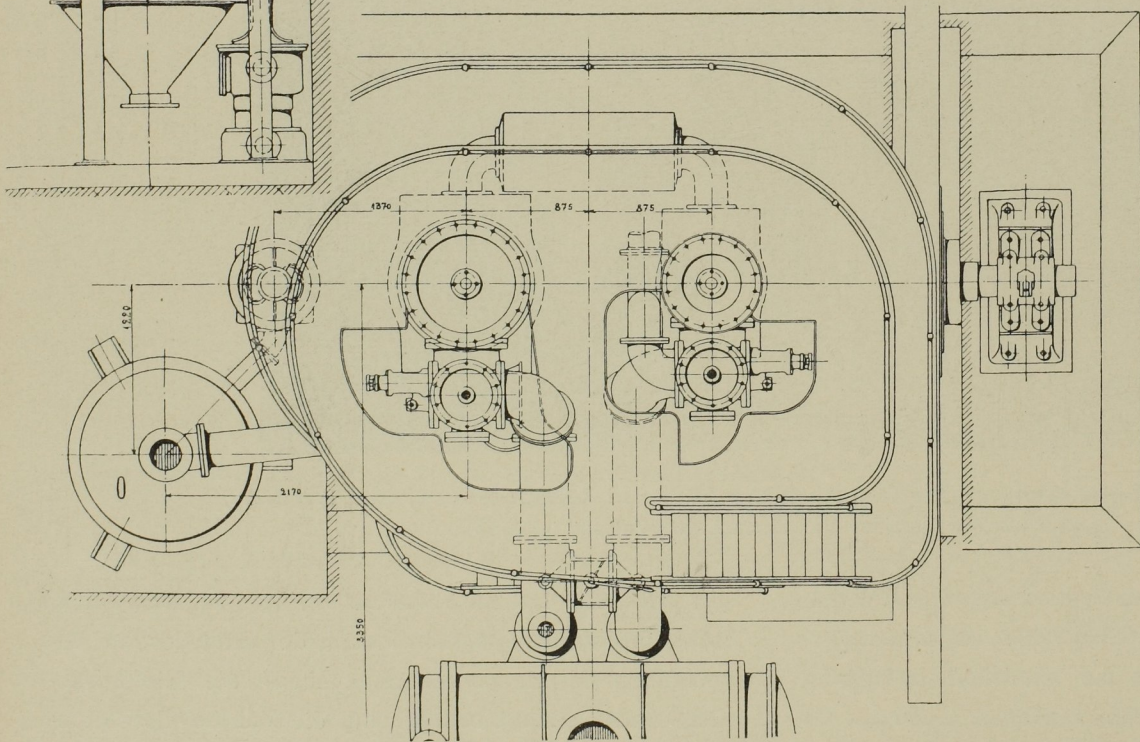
Stirnansicht und Grundriss. Massst. 1:50.
